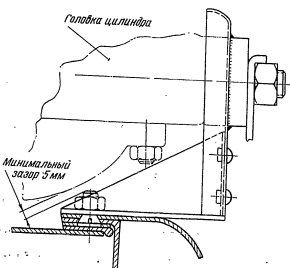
Установка кронштейнов капота на подкосы рамы двигателя. 1—вертикаль балочки; 2—тяги крепления кольца; 3—боковые профили.
